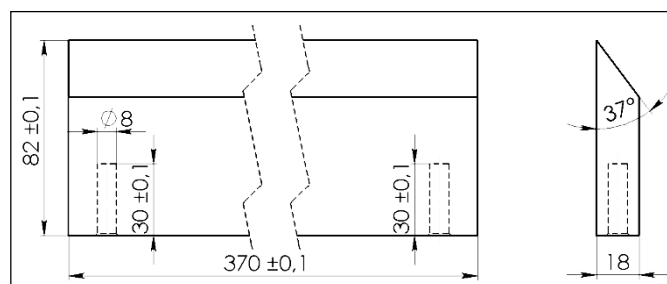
Нож плоский с прямолинейной режущей кромкой
